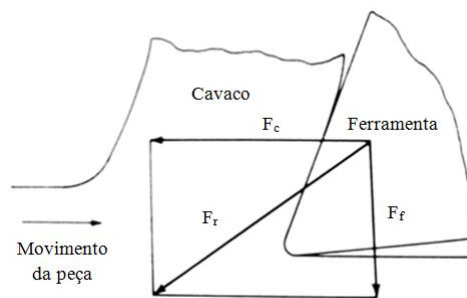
Componentes da força de usinagem  $F_c$  e  $F_f$  (Adaptado de BOOTHROYD; KNIGHT, 1989)
